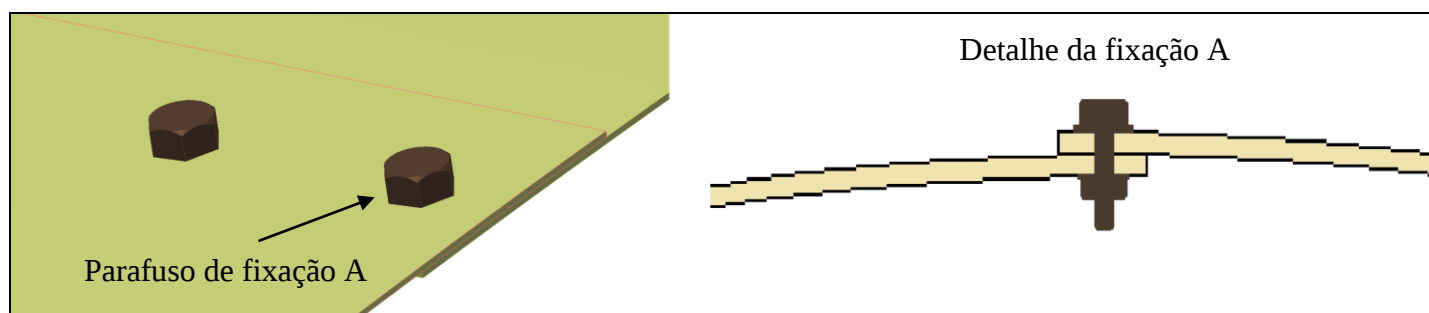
Detalhe com exemplo da fixação da junção da chapa metálica.
